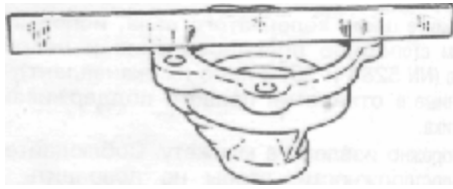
Корпус масляного насоса и детали — Двигатель В234F
